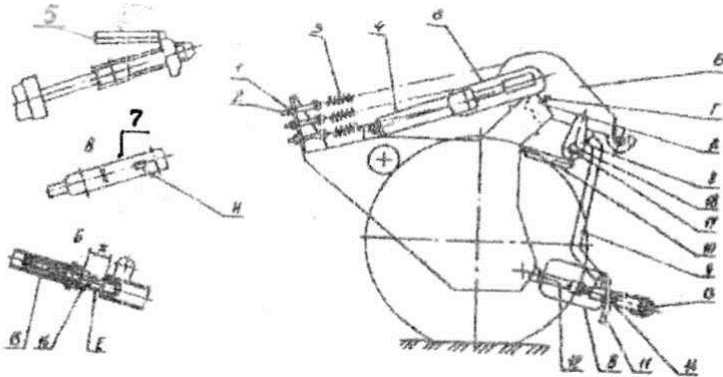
Механизмы вывешивания: 1 – гайка регулировочная; 2 – болт; 3 – пружина; 4 – фиксатор; 5 – крюк; 6 – скоба; 7 – гидроцилиндр; 8 – опора; 9, 10 – лига; 11 – фиксатор; 12 – балка; 13, 14 – ушко; 15 – резьбовой стержень; 16 – контргайка; 17 – шлицевой вал; 18 – колпак
